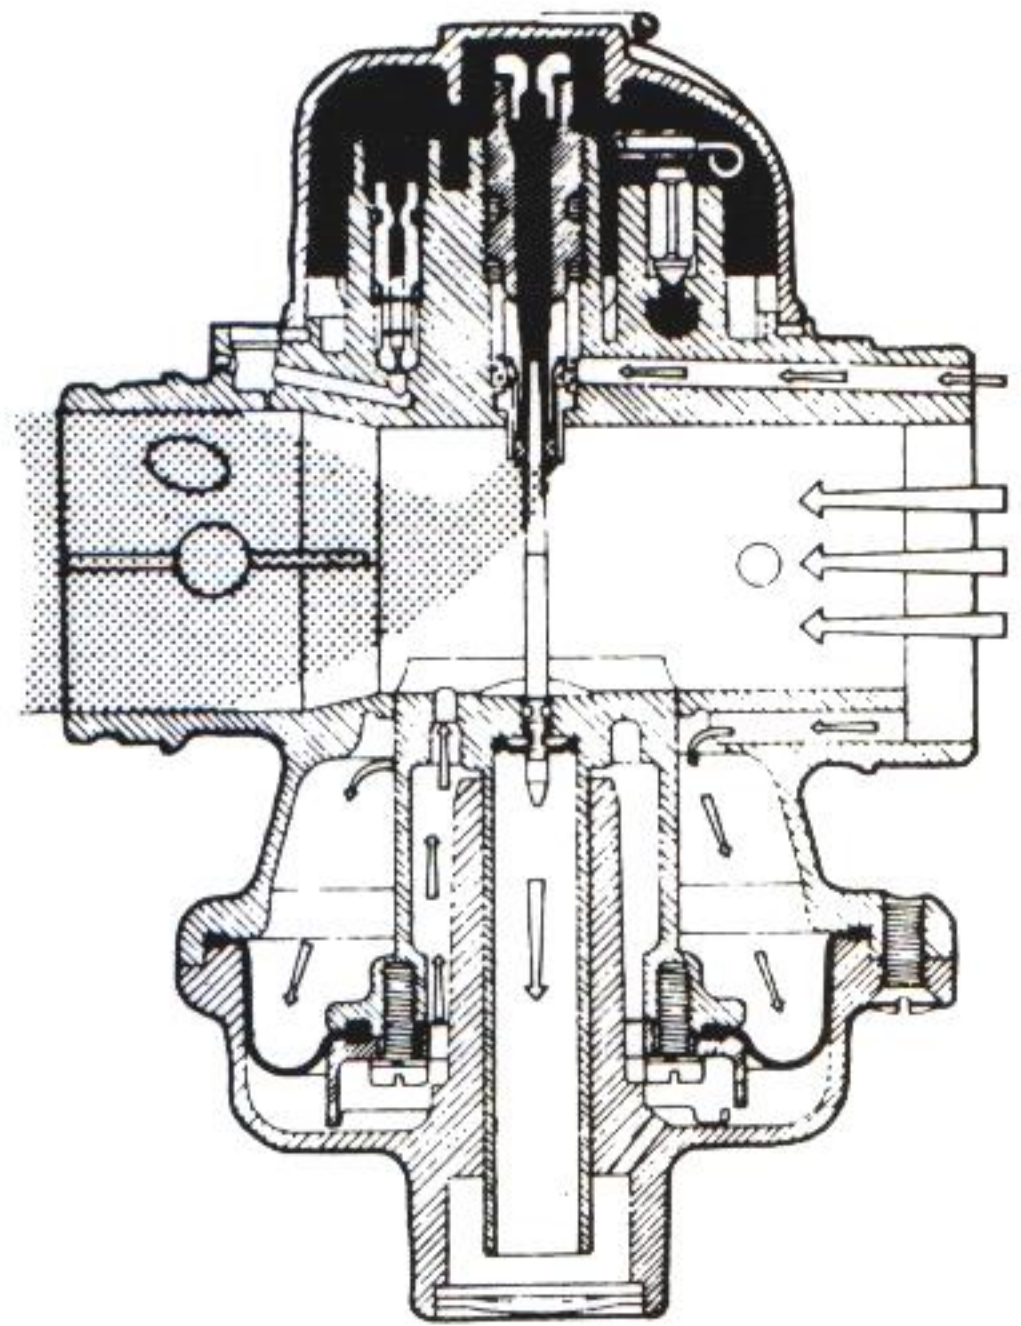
Esquema de funcionamiento del circuito principal en un carburador de la marca BING de cápsula de depresión.
